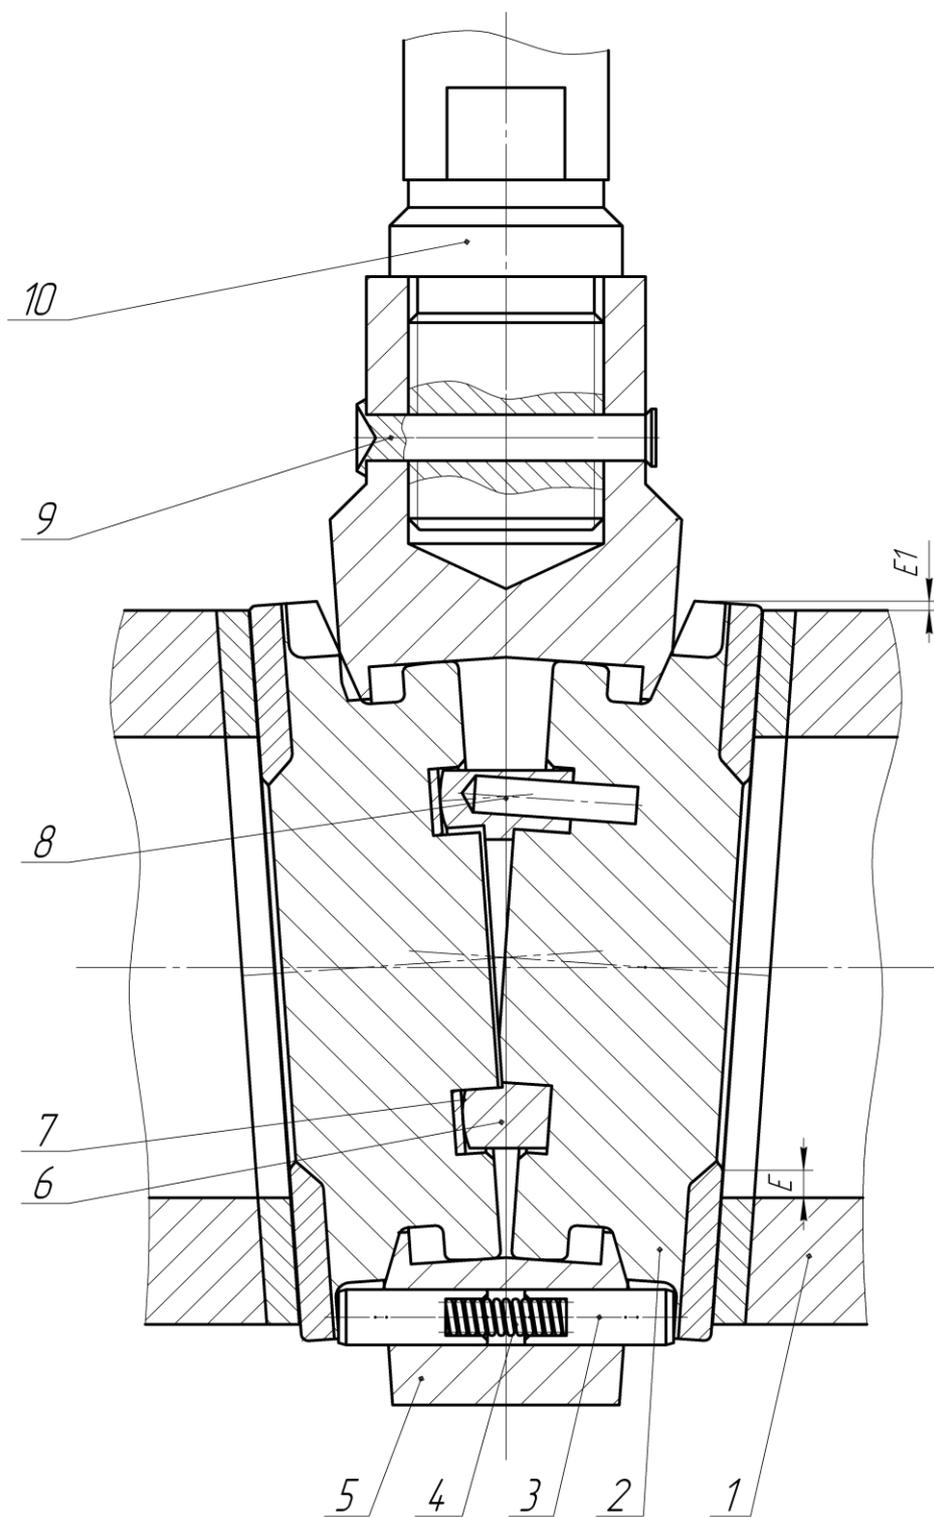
Запорный орган задвижек DN175 – DN325
